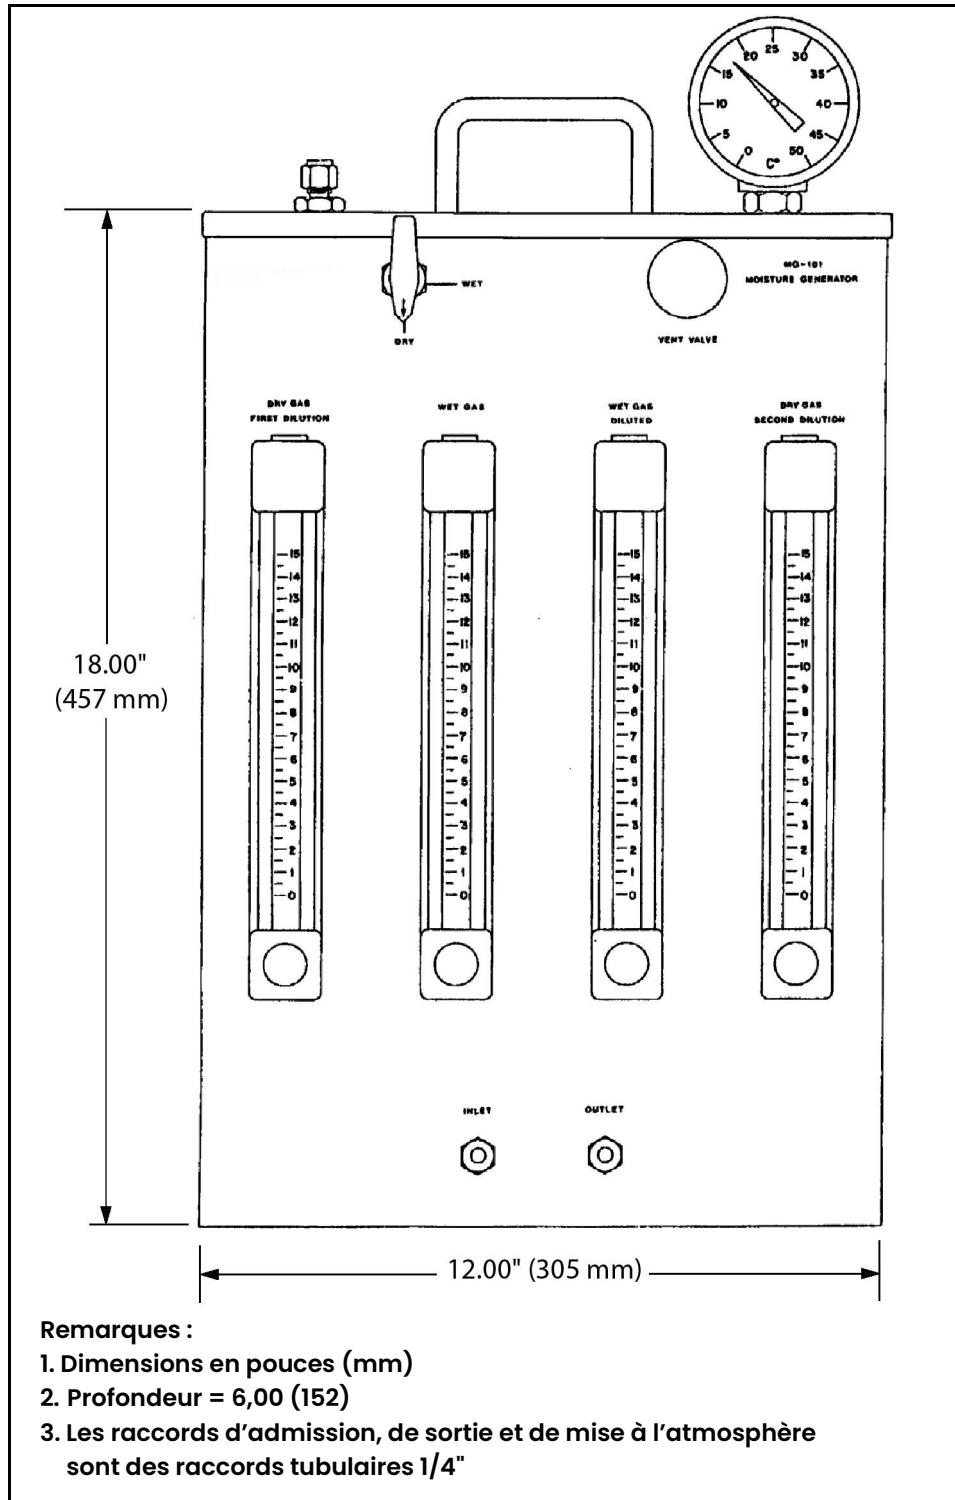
Dimensions hors-tout du générateur d'humidité MG-101
